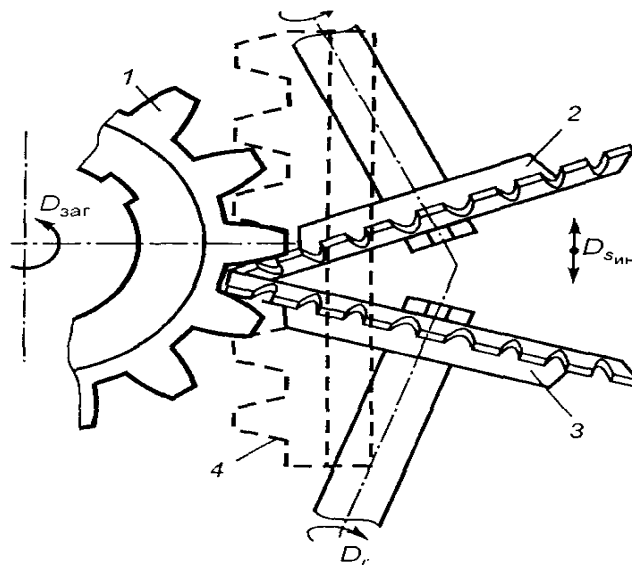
Схема нарезания зубьев конических колес двумя дисковыми фрезами
